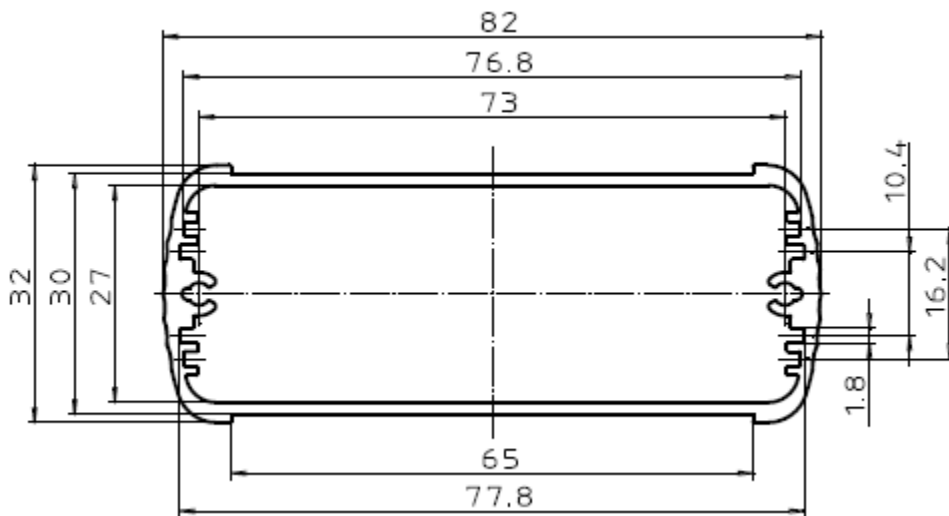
б. Чертеж профиля корпуса Устройства.
